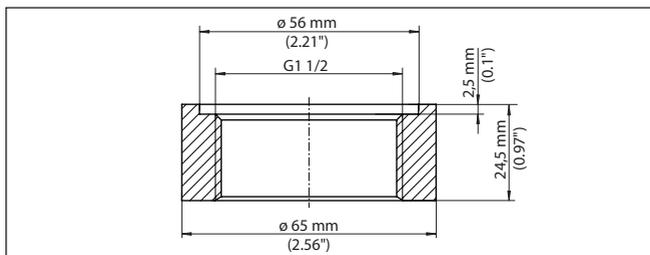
Dimensions raccord à souder filetage G1½ (DIN 3852-X)
